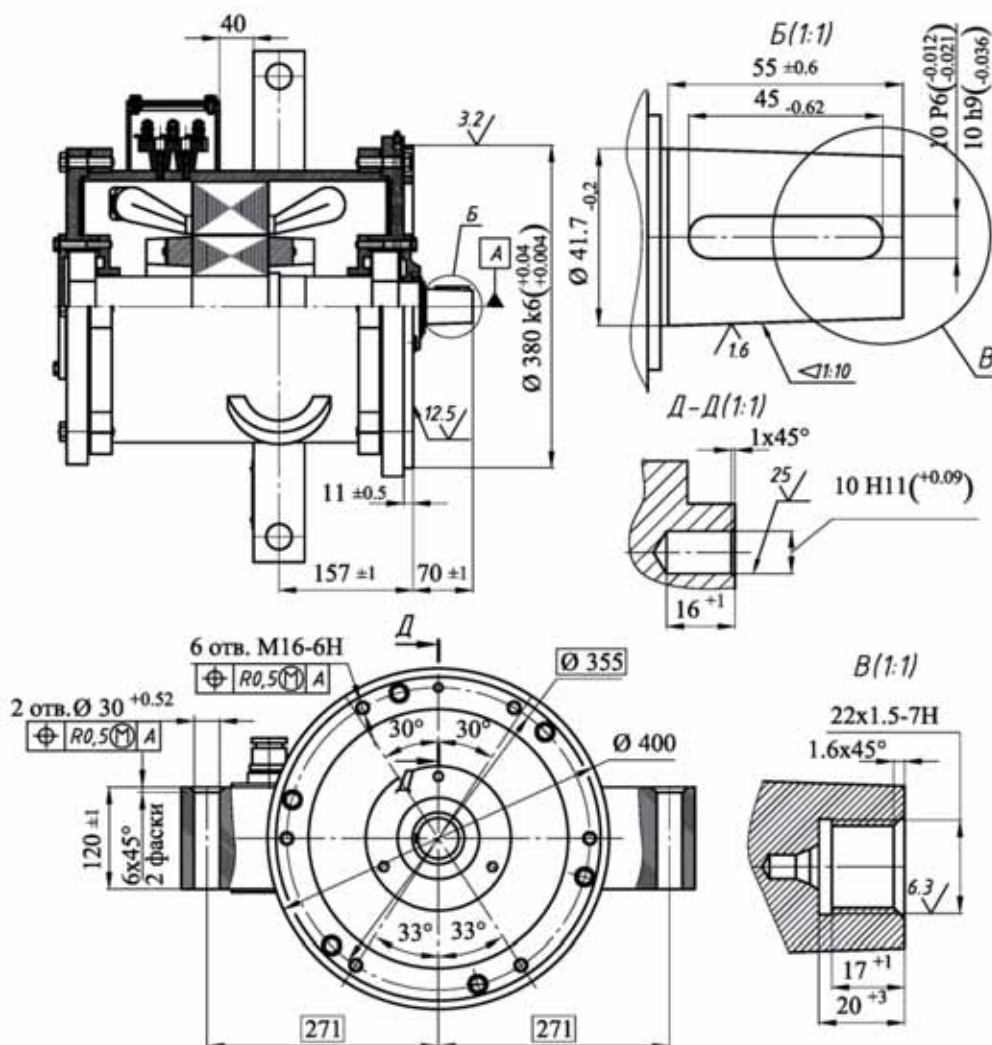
Габаритные и установочно-присоединительные размеры МАКУ160М6
